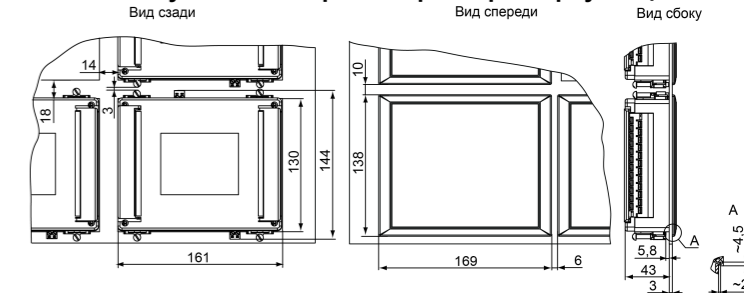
Прибор в корпусе Щ7, установленный в щит толщиной 3 мм
